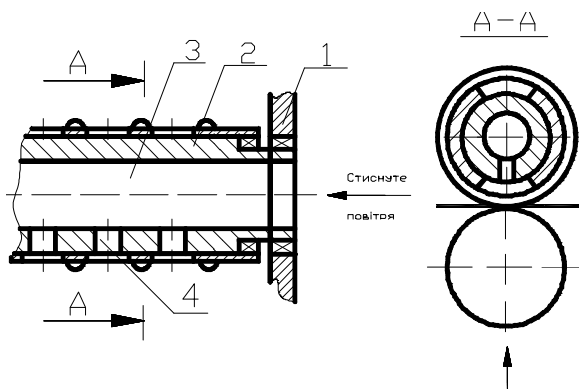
Конструктивна схема струменево-фрикційного живильника для довгомірних заготовок
